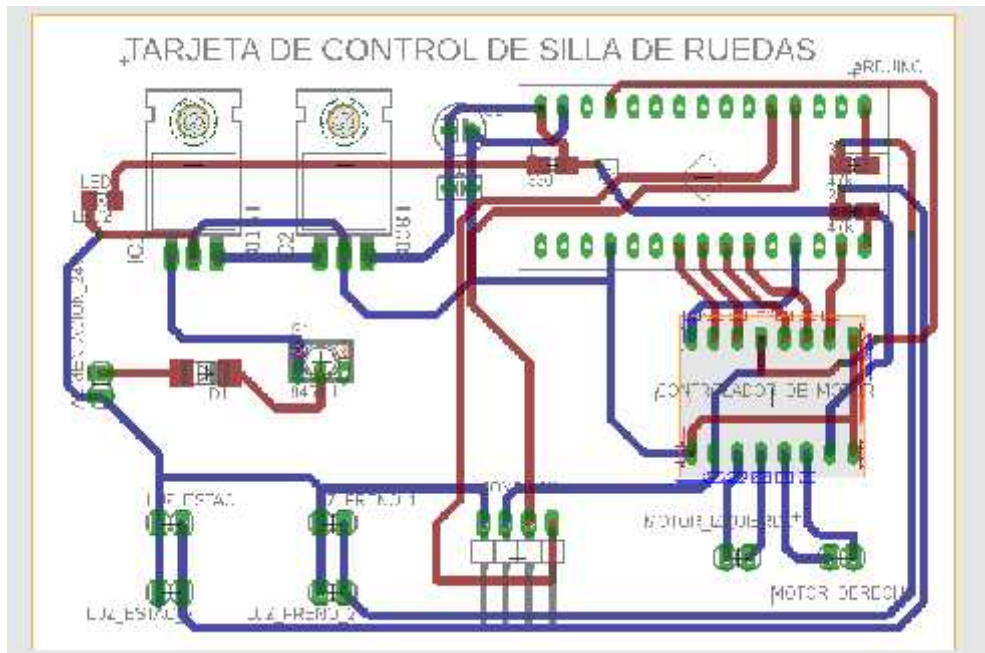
Diseño de la tarjeta de mando de la silla de ruedas
